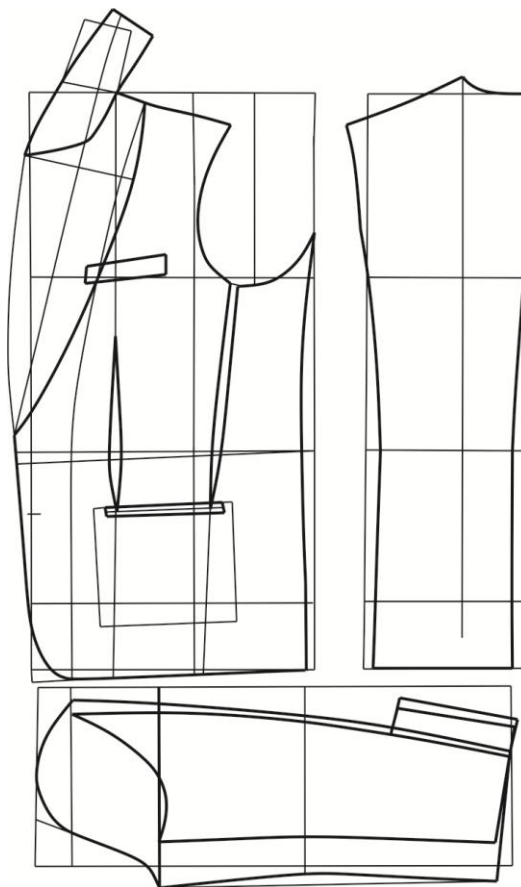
Чертеж конструкции мужского смокинга начала XXI века
